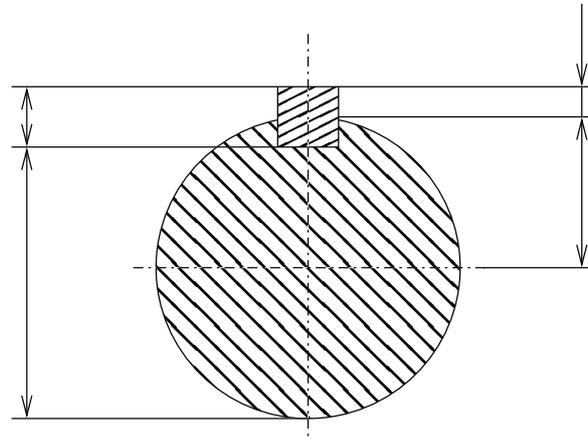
Vue en coupe d'un des 2 arbres et de sa clavette à compléter.
